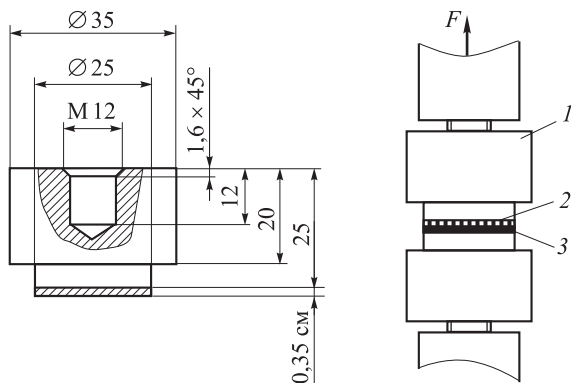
Схема испытаний плазменно-напыленных покрытий на отрыв:
